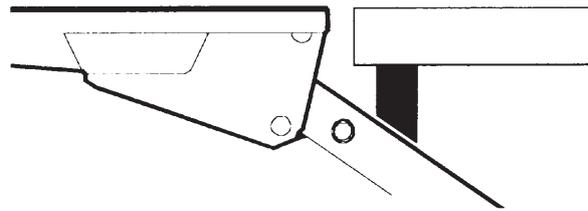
Placez les butées d'arrêt entre les bras de levage et la traverse arrière du plancher
